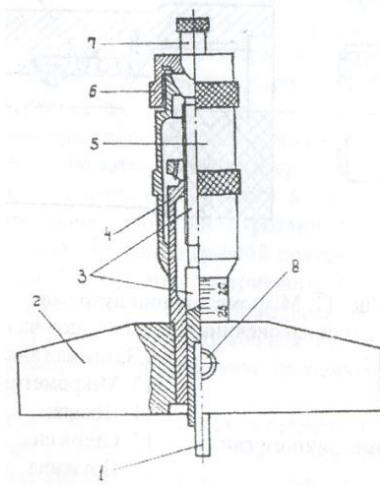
Мікрометричний глибиномір: 1 – вимірювальний стрижень; 2 – основа; 3 – Мікрометричний гвинт; 4 – стебло; 5 – барабан; 6 – ковпачок; 7 – тріскачка; 8 – штопор
